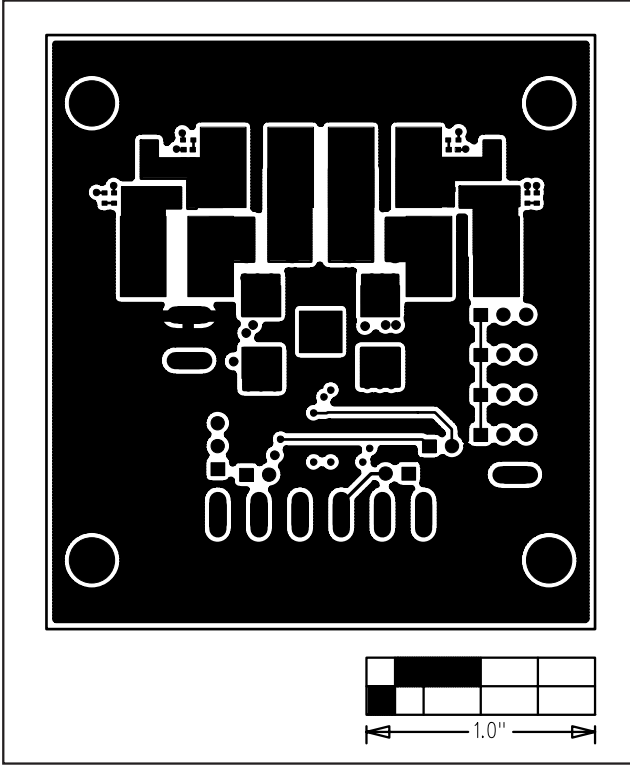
MAX9714 EV 키트 PCB 레이아웃 — 납땜 측
